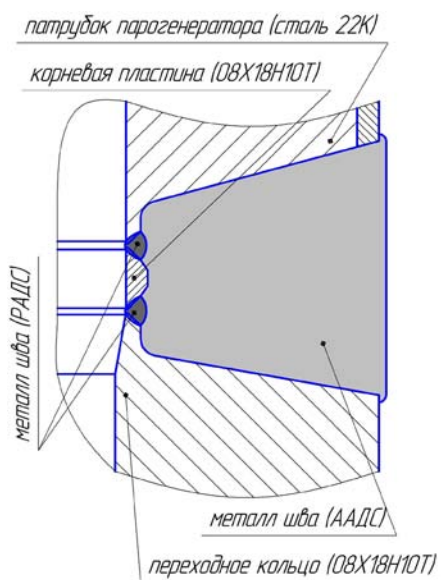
Отремонтированное сварное соединение автоматической сваркой
